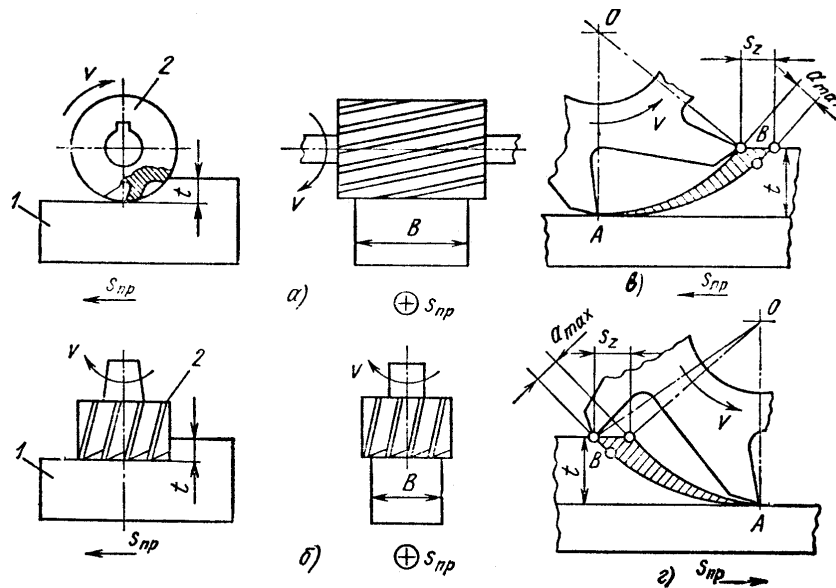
Схема фрезерования цилиндрической (а) и торцевой (б) фрезами, встречного (а) и попутного (г) фрезерования: 1 – заготовка, 2 – фреза
